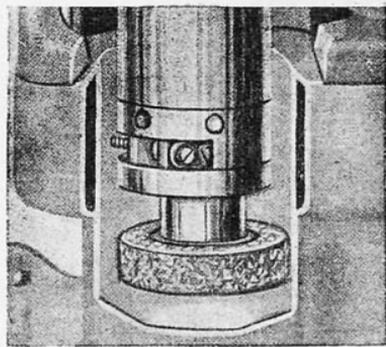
Шлифовка цилиндра с помощью станка Симплексити
